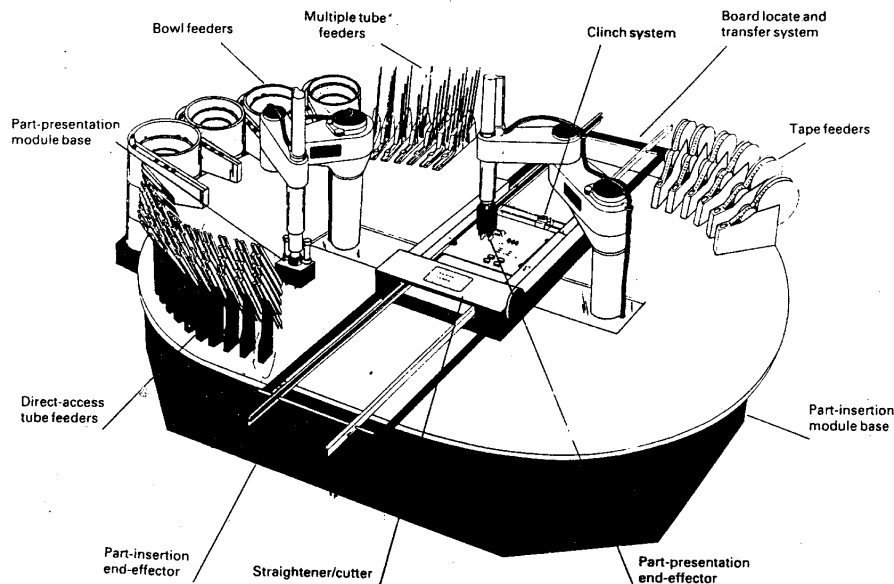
Estação de trabalho robotizada para montagem de componentes em placas de circuito impresso (PCB) (Ref. in Assembly Automation, Vol8,nº3, pp 127-129)
